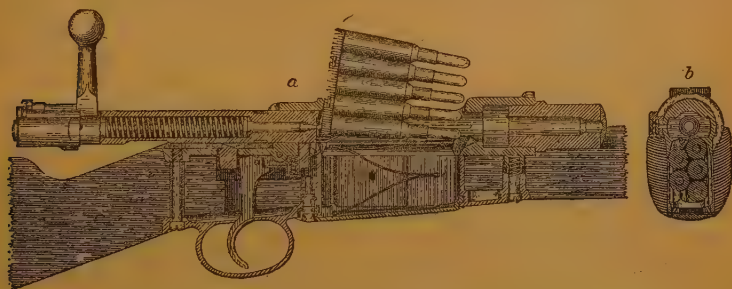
a. Senkrechter Längsschnitt durch den Schloßmechanismus, Kammer geöffnet; b. Senkrechter Querschnitt durch das gefüllte Magazin.
